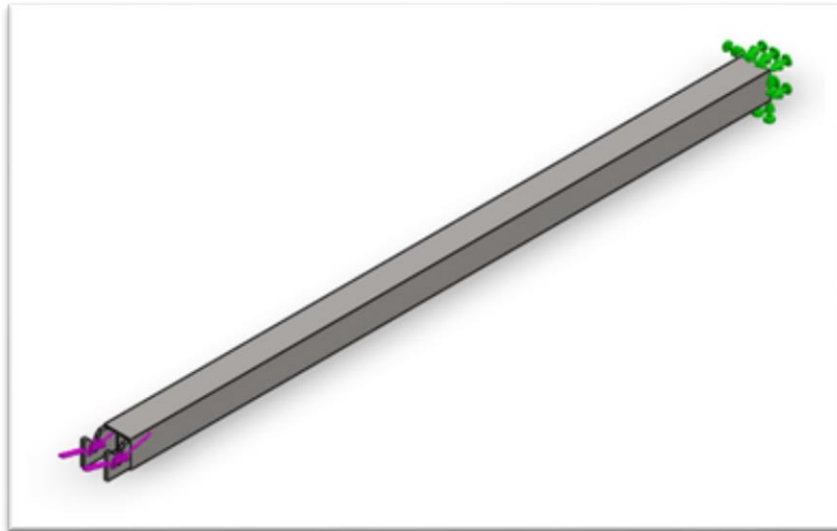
Modelo simplificado da viga do braço de alavanca – Teste de Içamento carretel de 28'
